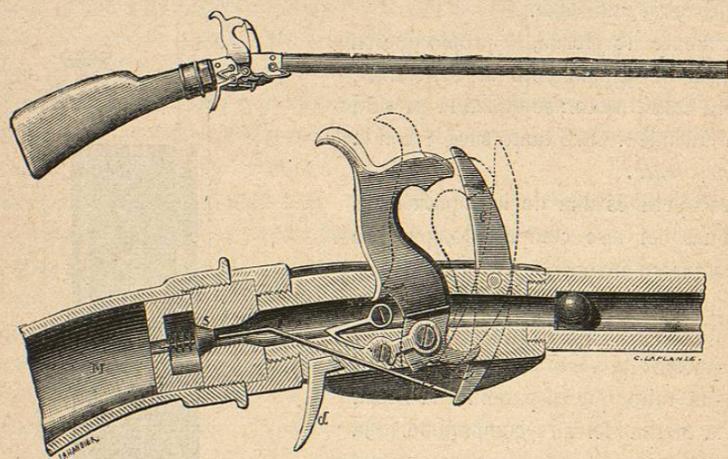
Escopeta de viento (vista exterior y sección longitudinal)
